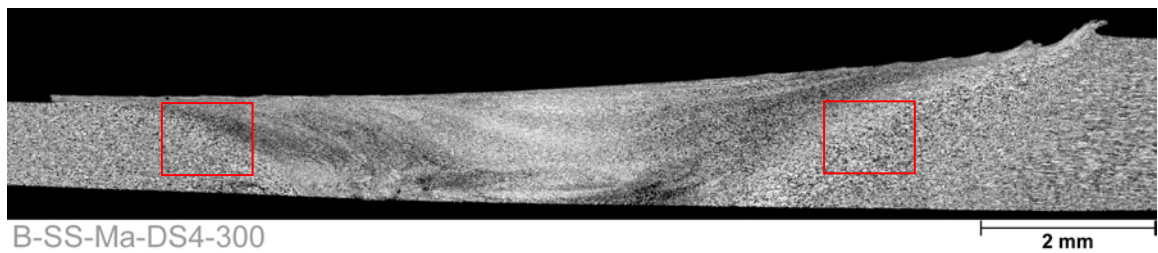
Macrografia de uma junta 5754 H22 soldada com 1 m/min. Ataque químico: Barker.
